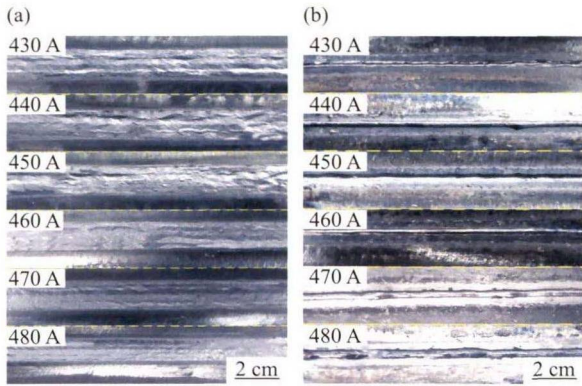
焊接接头表面外观形貌。(a)焊接接头正面成形;(b)焊接接头背面成形
